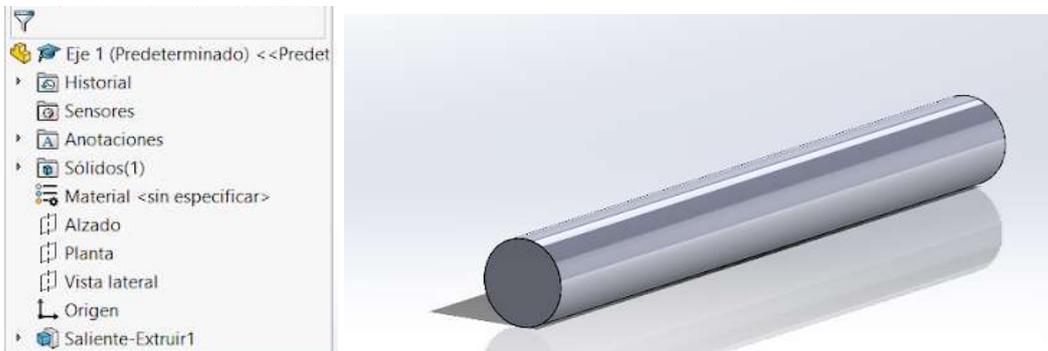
Captura de pantalla SolidWorks, extrusión pieza 3. Elaboración propia.
